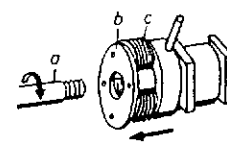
Roscado por cilindrado mediante grueso cabezal de rodillos. a) Pieza; b) cabezal con rodillos; c) rodillos. La rosca es laminada o cilindrada mediante tres rodillos. La cabeza portarodillos se abre automáticamente después de ejecutar la rosca.
